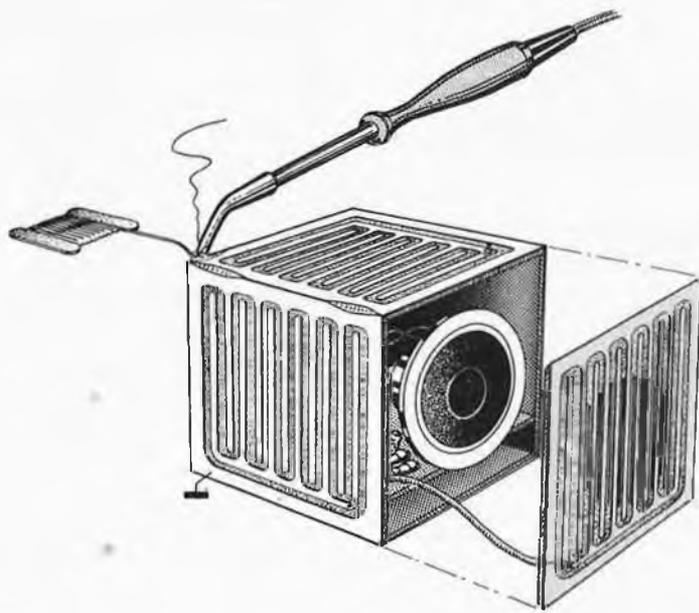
Voici à quoi peut ressembler votre cube musical une fois son assemblage terminé. La dernière facette n'est soudée qu'aux quatre coins de façon à pouvoir changer de pile aisément. Notez au passage la technique choisie pour transformer une face en touche sensible.
